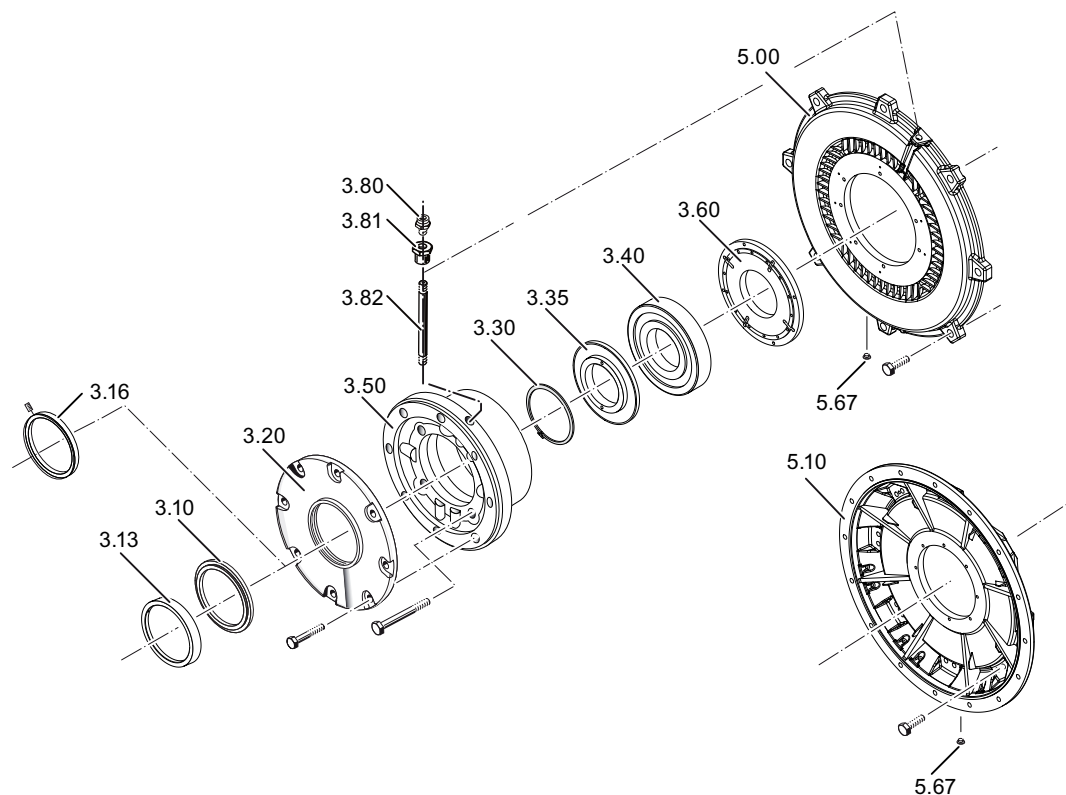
Подшипник качения, приводная сторона (DE) с корпусом подшипника
